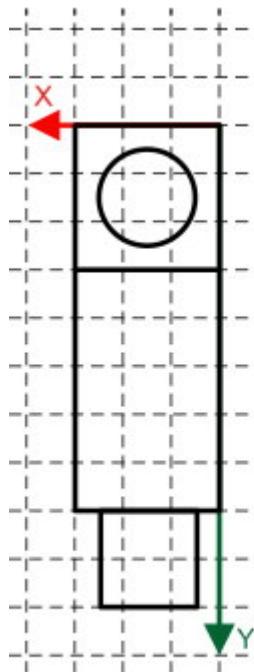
Grundriss eines Werkstücks
